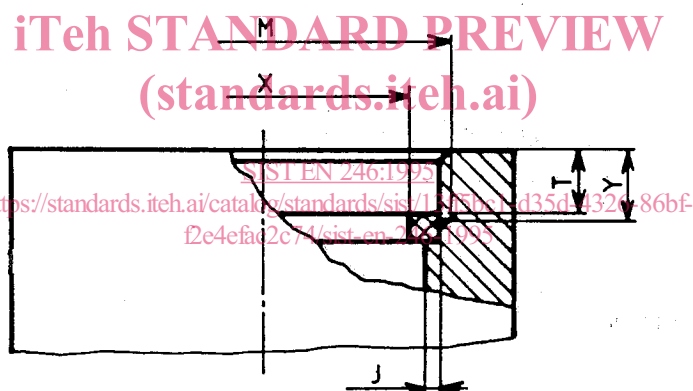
Strahlregler mit Anschluß mit Innengewinde
